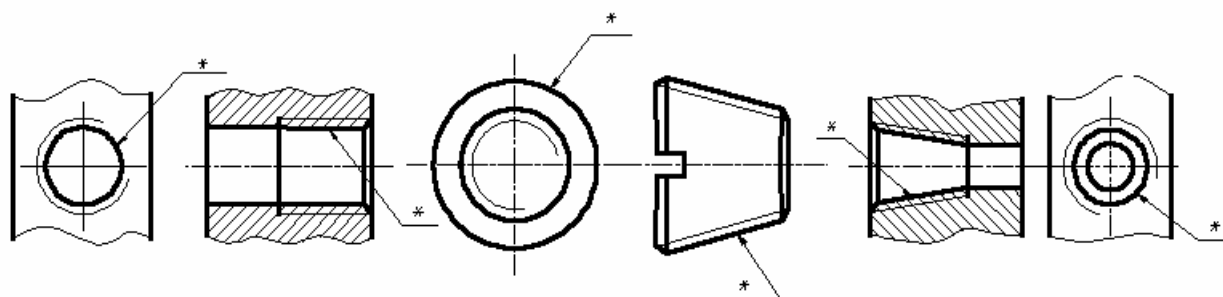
Обозначение трубной цилиндрической и конической резьбы.
